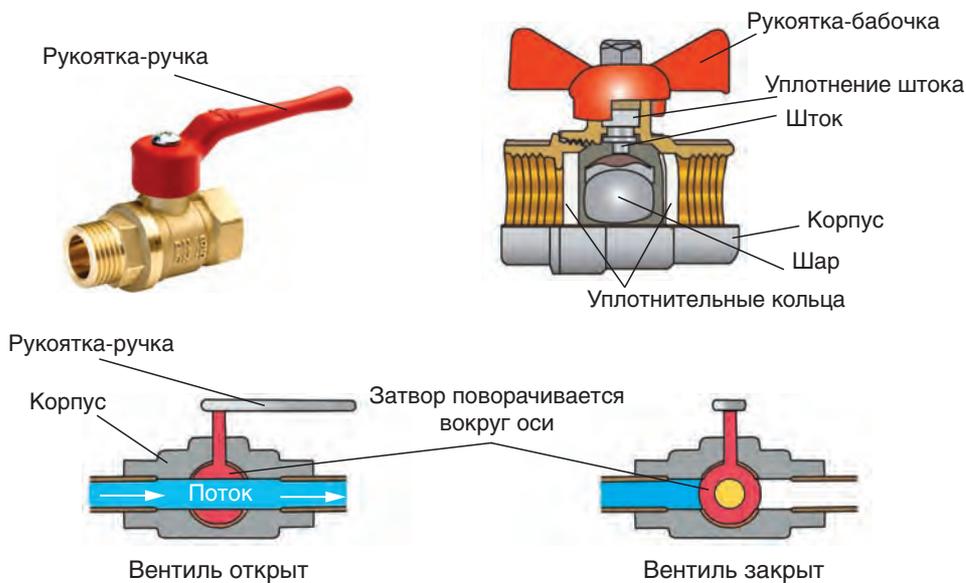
Шаровый вентиль: общий вид, устройство (вверху) и принцип работы (внизу)
